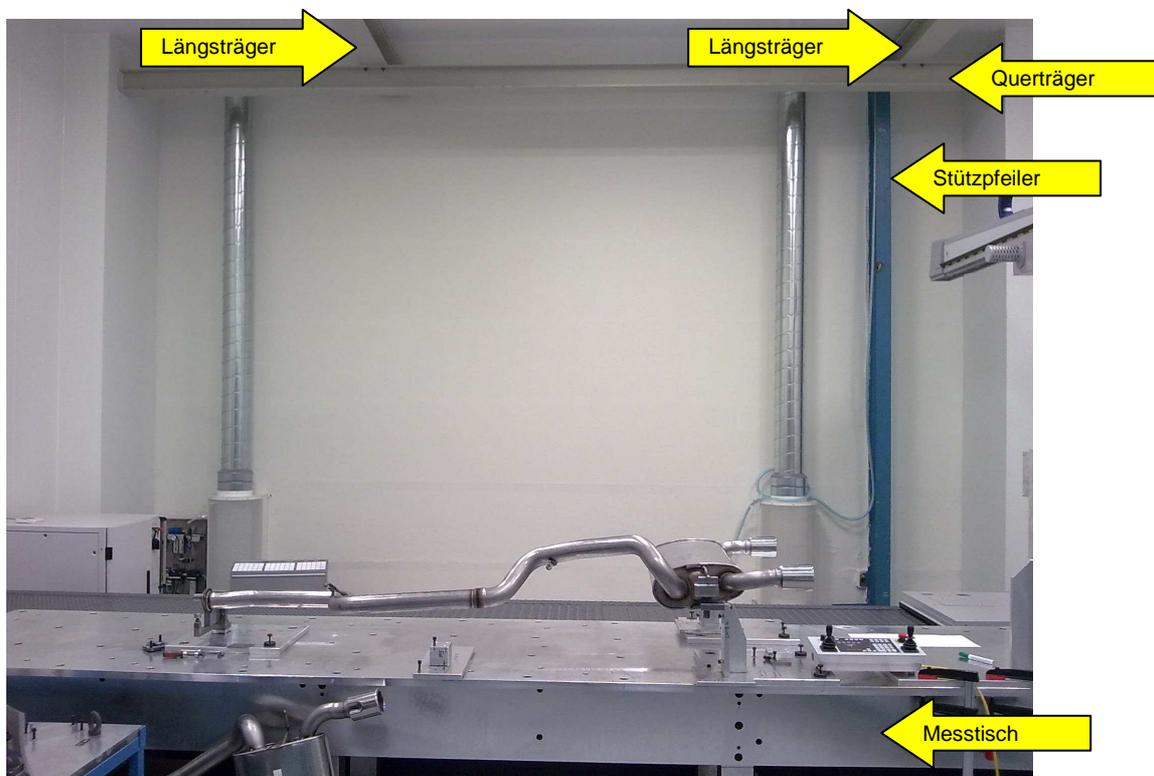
Stahlkonstruktion kleiner Lastenkrans
